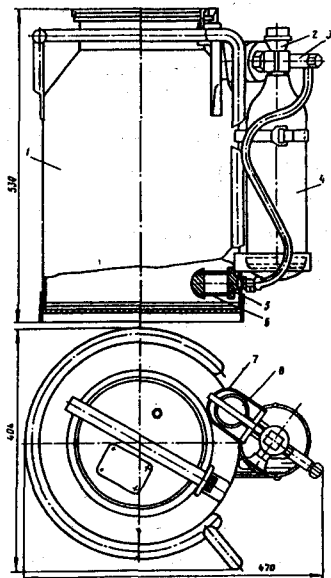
Контейнер для транспортировки личинок и молоди рыб: 1 - флага; 2 - редуктор; 3 - игольчатый клапан; 4 - кислородный баллон; 5 - корпус аэрационного узла; 6 - распылитель аэрационного узла; 7 - защитный кожух; 8 - манометр
